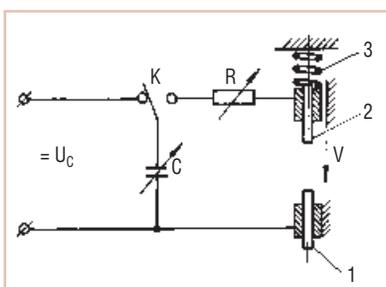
Схема процесса УКС: 1 — неподвижная деталь; 2 — деталь, движущая со скоростью V ; 3 — приводная пружина; U_C — напряжение зарядки конденсаторов; C — конденсаторы; K — ключ, переключающий конденсаторы с зарядки на разряд; R — резистор, управляющий характеристиками процесса
